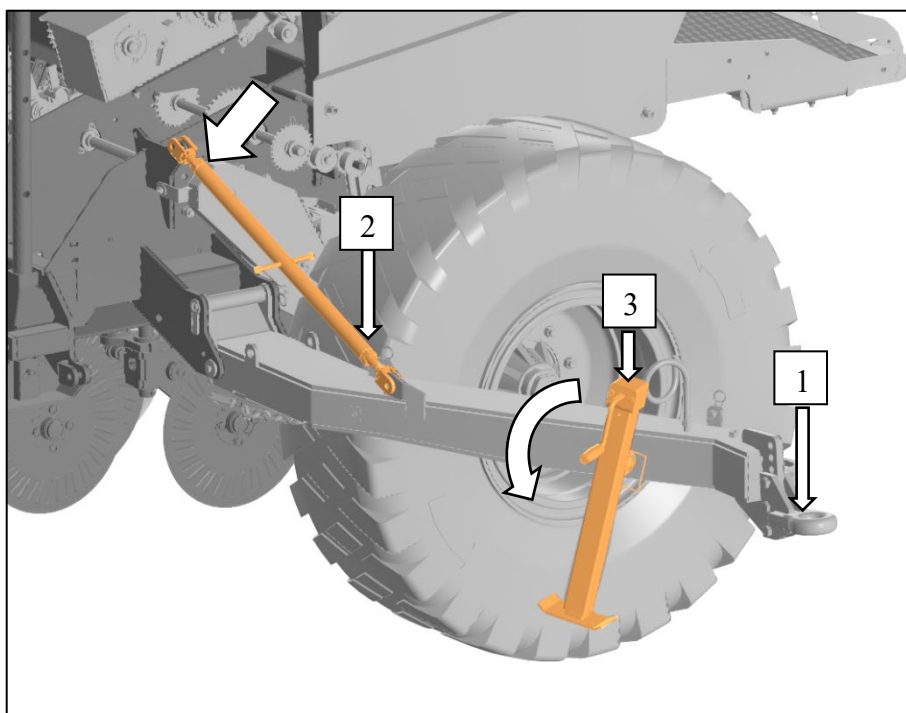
Установка тяги и подножки бокового фаркопа
